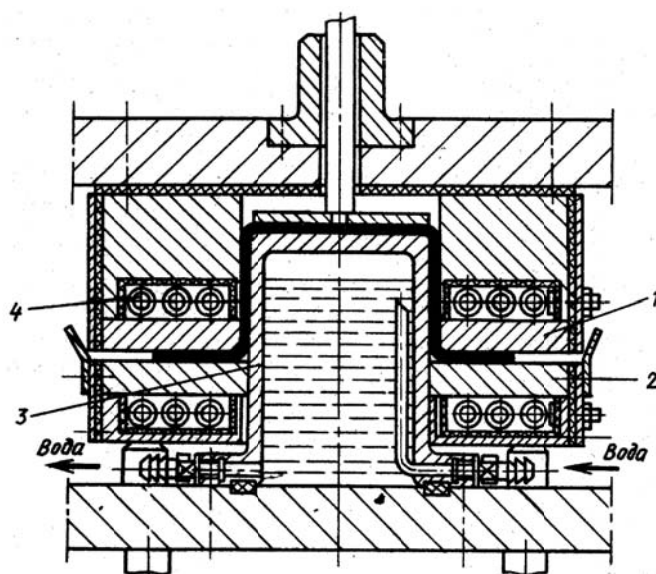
Схема штампа для вытяжки с нагревом зоны пластической деформации:
